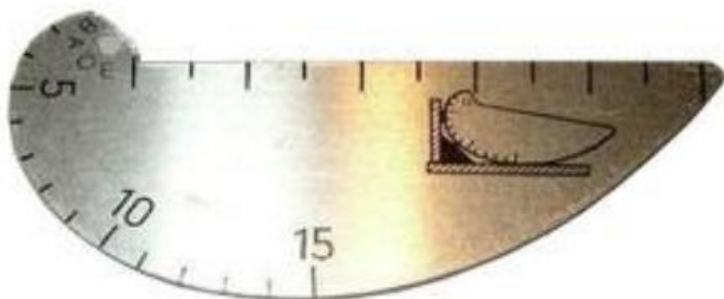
Универсальный шаблон Красовского для визуального и измерительного контроля тавровых, стыковых и нахлесточных сварных соединений, а также измерения зазора между кромками свариваемых деталей и высоты усиления шва.
